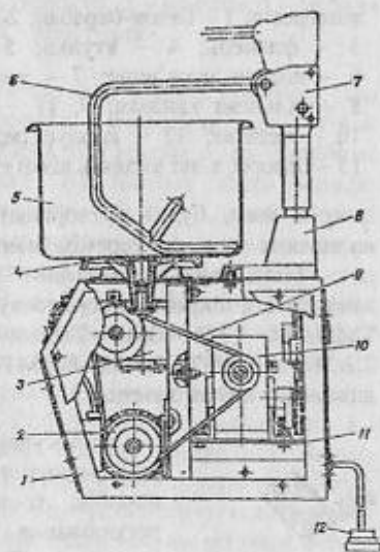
Тістомісильна машина ТММ-60М: 1 – корпус; 2 – електродвигун; 3, 10 – редуктори одноступінчасті черв'ячні; 4 – диск; 5 – діжа; 6 – важіль місильний; 7 – головка місильного важеля; 8 – корпус; 9 – передача клинопасова; 11 – болти; 12 – рознімач штепсельний
